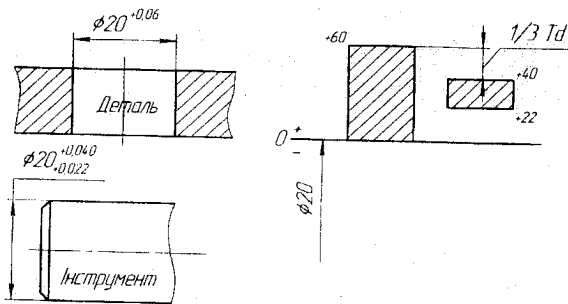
Зв'язок допуску на інструмент з допуском на розмір деталі
